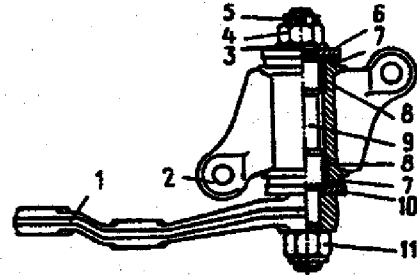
Conjunto da alavanca oscilante: 1 - alavanca oscilante; 2 - suporte do mancal; 3 - arruela; 4 - porca de ajuste; 5 - cavilha; 6 - arruela superior; 7 - junta; 8 - casquilho; 9 - eixo da alavanca; 10 - arruela inferior; 11 - porca auto-travante.
